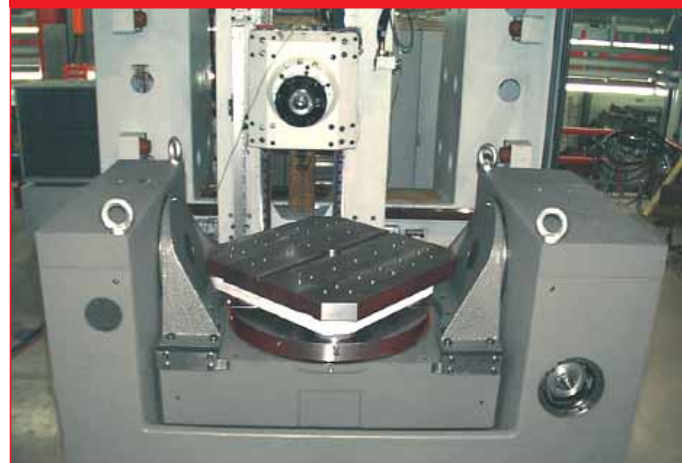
Наклонно-поворотный стол станка JIG 1200
